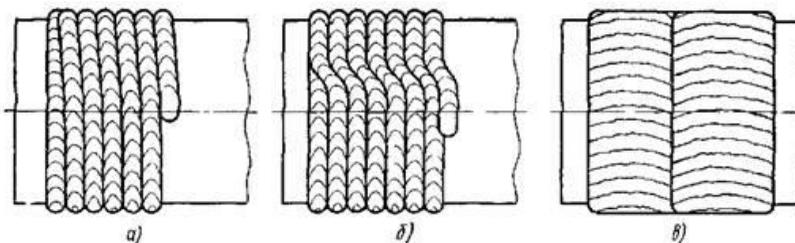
Наплавка тел вращения: а – по винтовой линии; б – кольцевыми валиками с прерывистым смещением на шаг; в – широкими кольцевыми валиками
